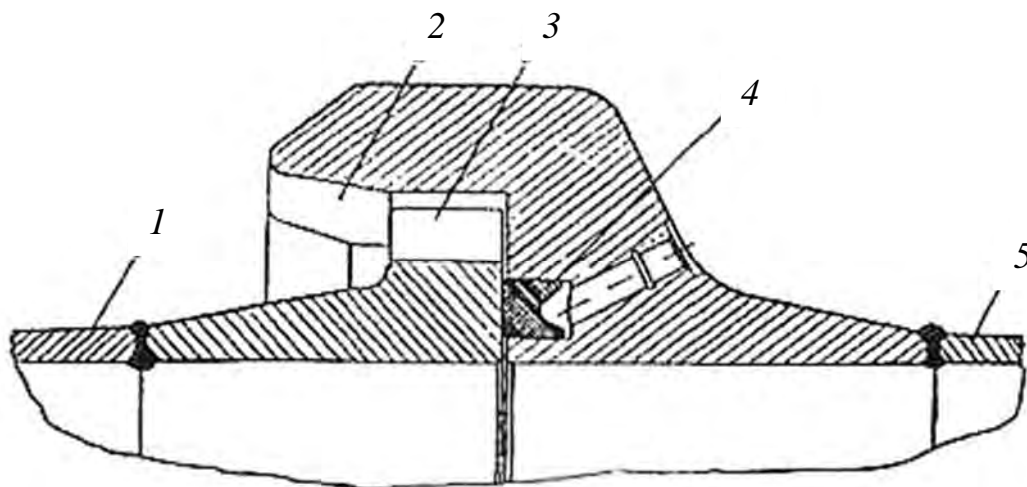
Байонетный затвор крышки: 1 – корпус крышки; 2 – зуб венца; 3 – зуб крышки; 4 – уплотнение; 5 – корпус автоклава
